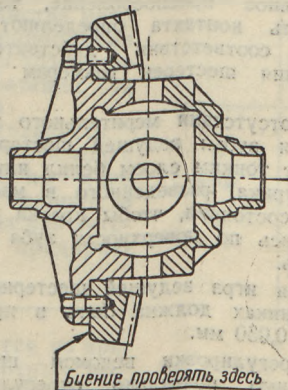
Проверка биения «затылка» ведомой шестерни.
